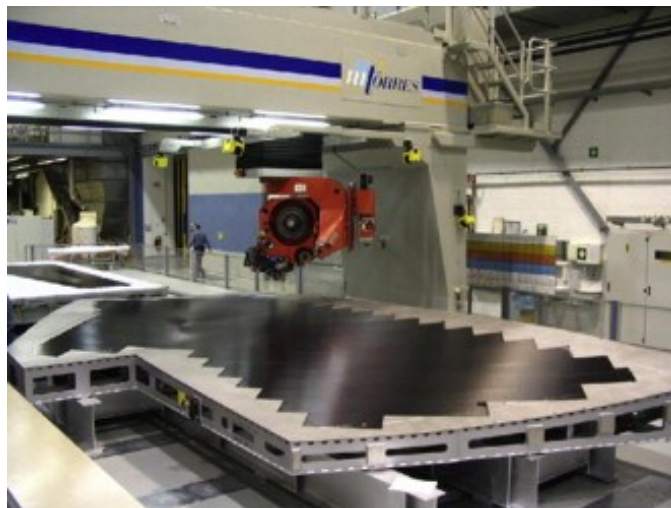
Sistema ATL, aplicação de fibra sobre um molde plano [61]
